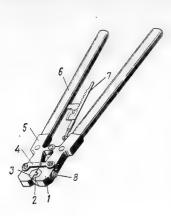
1— головка; 2— матрица; 3— пуансон; 4— рычаг подвижный; 5— устройство блокирующее; 6— рычаг неподвижный
